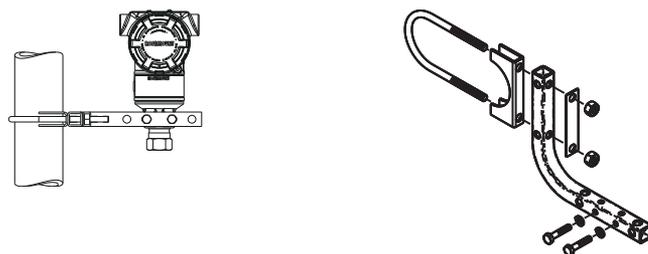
Montaggio su palina con flangia coplanareFigura 2-3: Montaggio su pannello con flangia tradizionaleFigura 2-4: Montaggio su palina con flangia tradizionale
